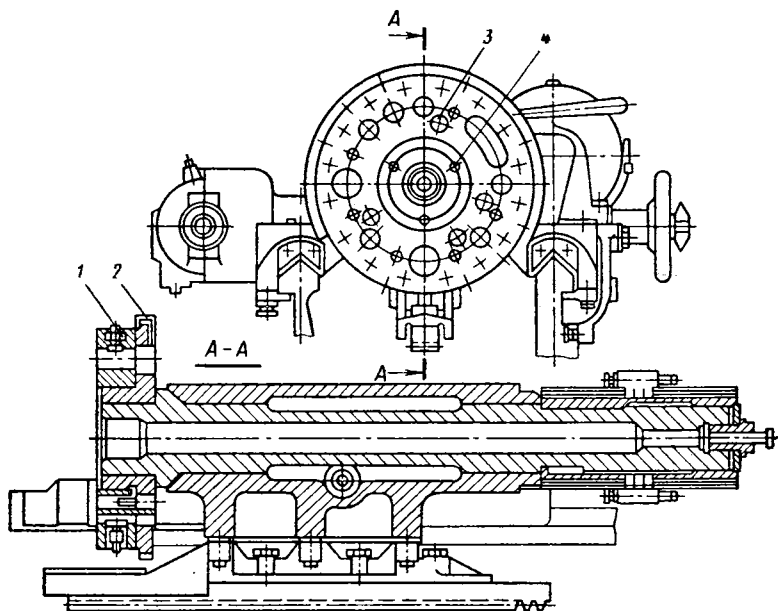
Прикрепление револьверной головки к зубчатому колесу
